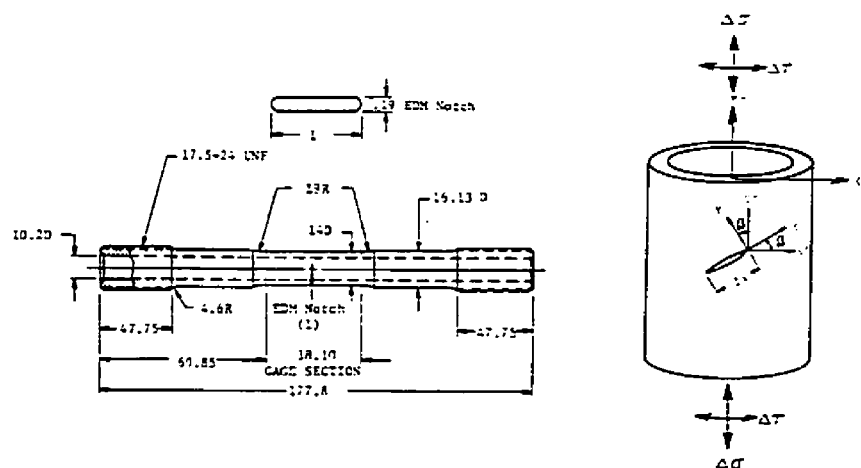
Éprouvette de traction-torsion et le repère de l'entaille (dimensions en mm)
